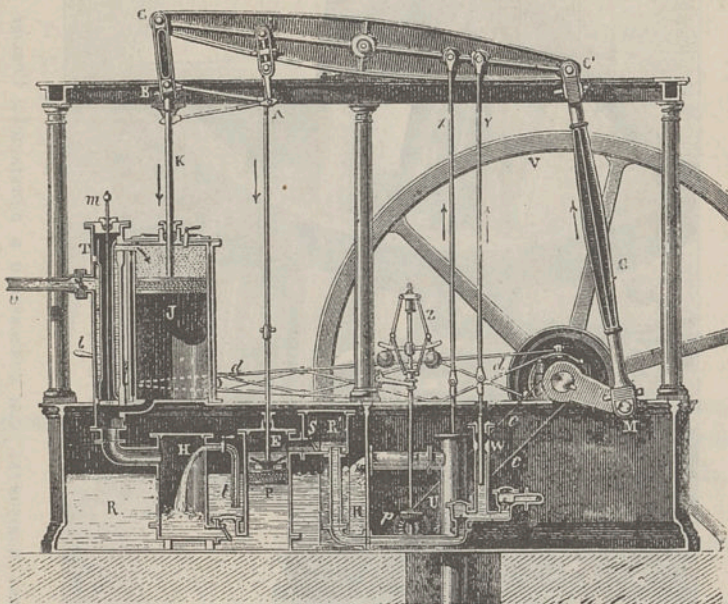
MACHINA DE BALANCEIRO DE WALT COM CONDENSADOR
